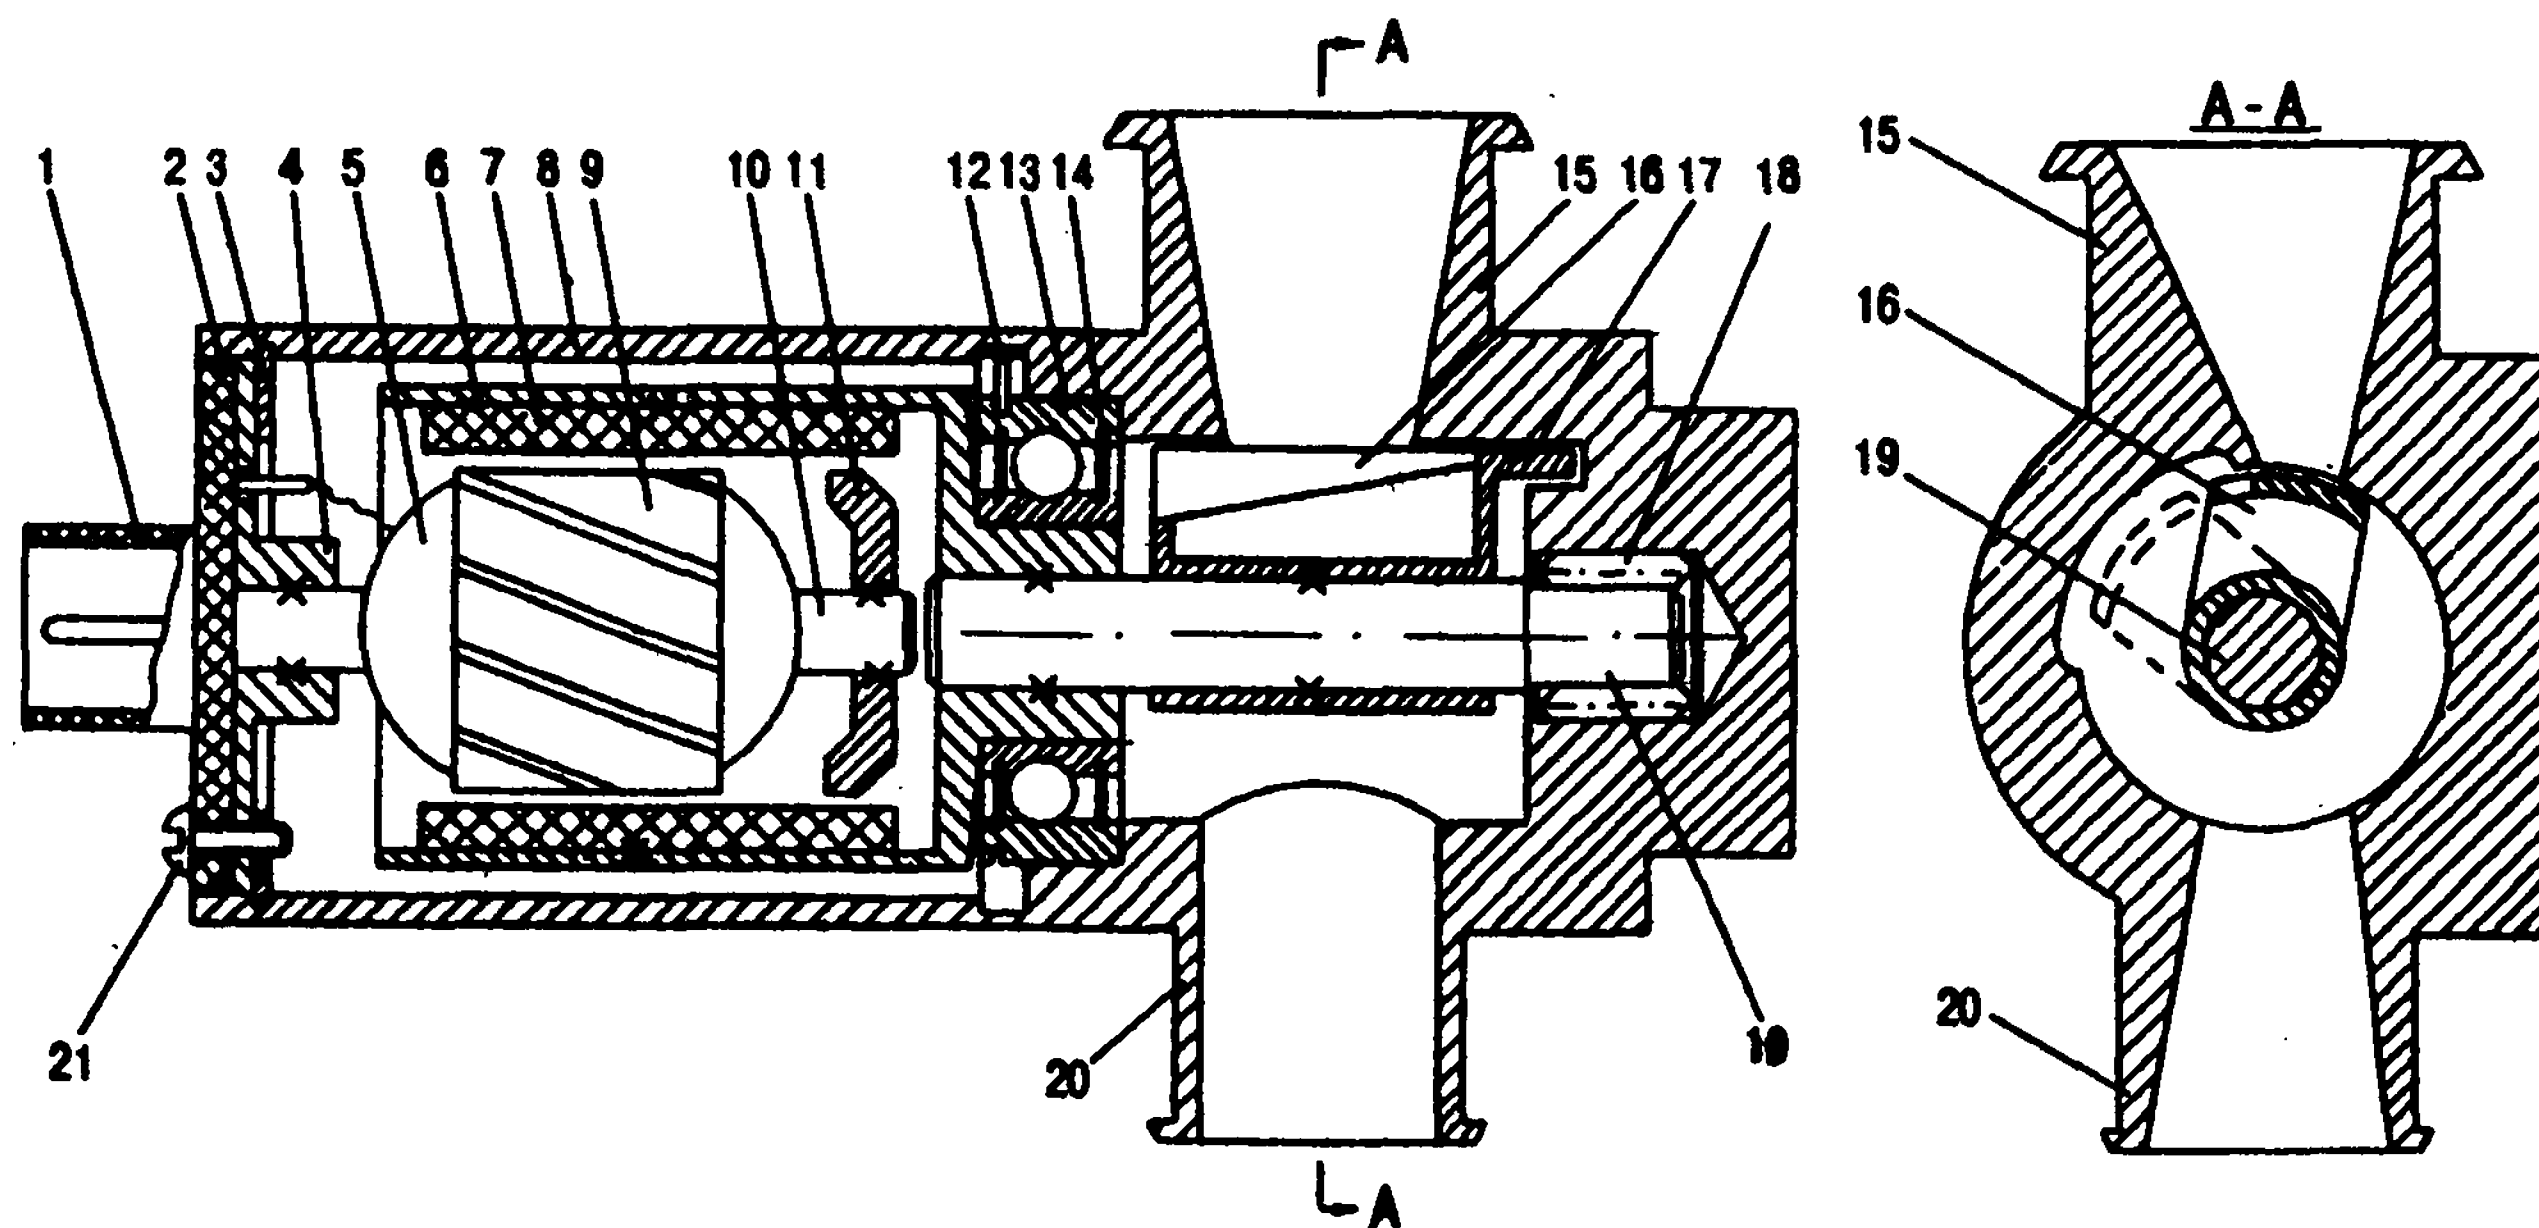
Регулятор дополнительного воздуха: 1 - штекерная колодка, 2 - уплотнительное кольцо, 3 - шайба крепления, 4 - фланец крепления оси якоря, 5 - обмотка якоря, 6 - поворотный стакан, 7 - магнит, 8 - корпус, 9 - якорь неподвижный, 10 - ось якоря, 11 - магнитопровод, 12 - стопорное кольцо подшипника, 13 - шариковый подшипник, 14 - уплотнение подшипника, 15 - патрубок входной, 16 - поворотная заслонка, 17 - упор, 18 - роликовый подшипник, 19 - вал заслонки, 20 - патрубок выходной, X - соединение неразъемное
